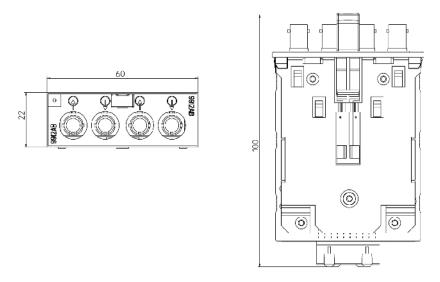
MM900 Dessin coté 3 : Ports BFOC
